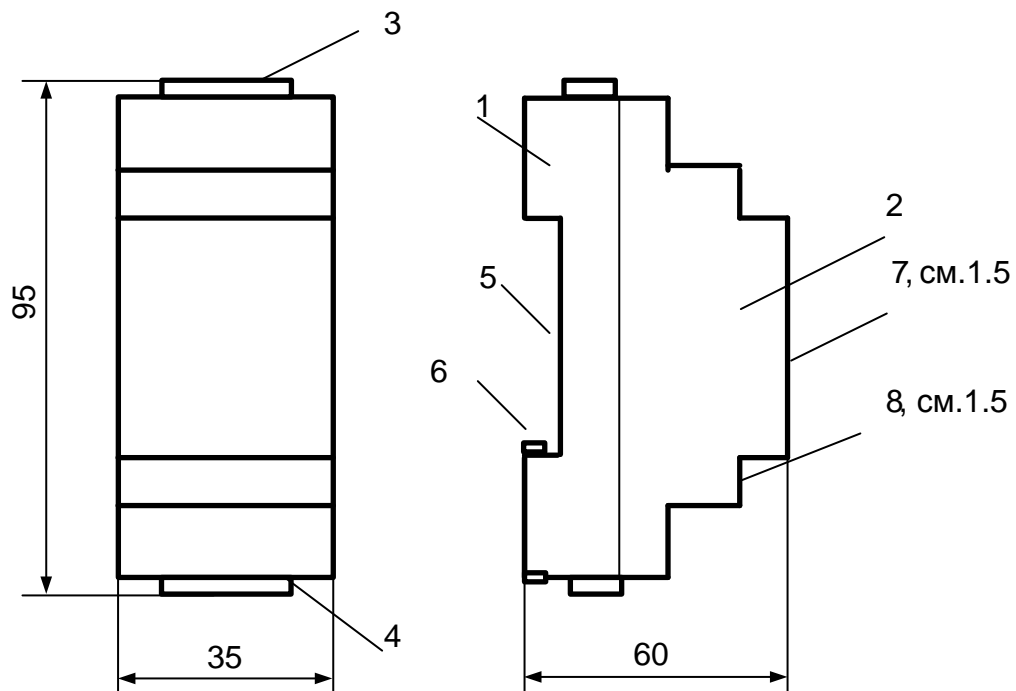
габаритные и установочные размеры преобразователя ЧИС
